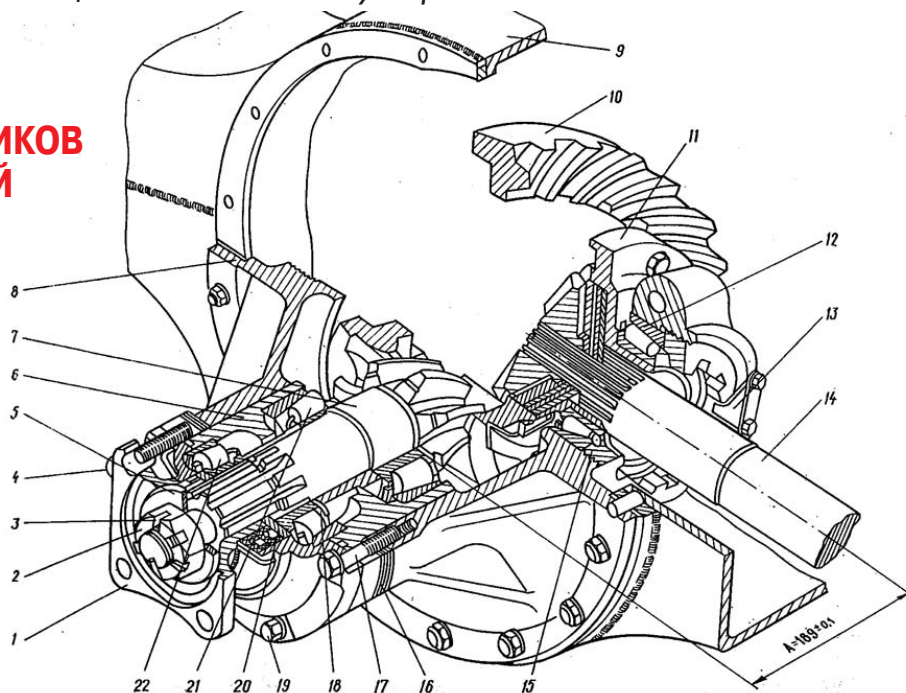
Регулировка главной передачи: 1 — фланец; 2 — гайка; 3 — шплинт; 4, 17, 19 — болт; 5 — шайба; 6 — стакан; 7 — шестерня ведущая; 8 — корпус главной передачи; 9 — корпус моста; 10 — шестерня ведомая; 11 — дифференциал; 12, 21, 22 — подшипник; 13 — крышка подшипника; 14 — полуось; 15 — гайка регулировочная; 16, 18 — прокладка регулировочная; 20 — крышка
